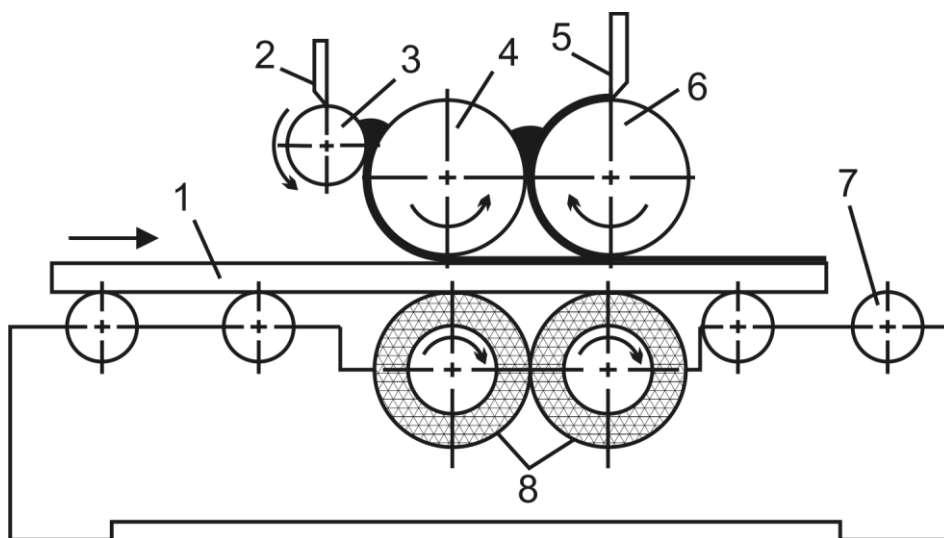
Технологическая схема вальцово-рабельного станка для грунтования и штатлевания пластей щитовых деталей: 1 - деталь; 2, 5 - ракели; 3 - дозирующий валец; 4 - наносящий валец; 6 - втирающий валец; 7 - роликовый конвейер; 8 - подающие вальцы
